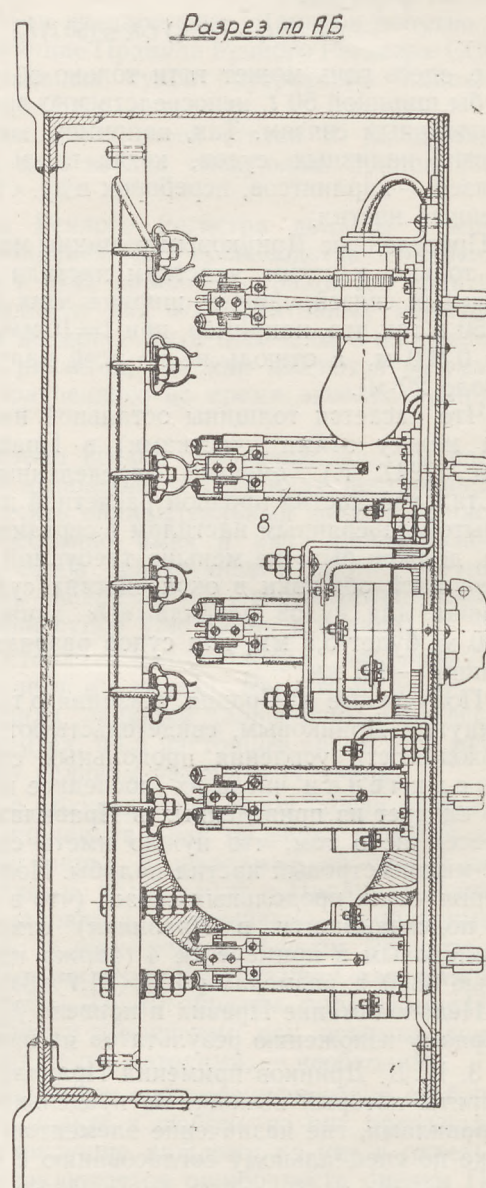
Боковой вид станции питания (разрез по АБ); 8 — дробсы
